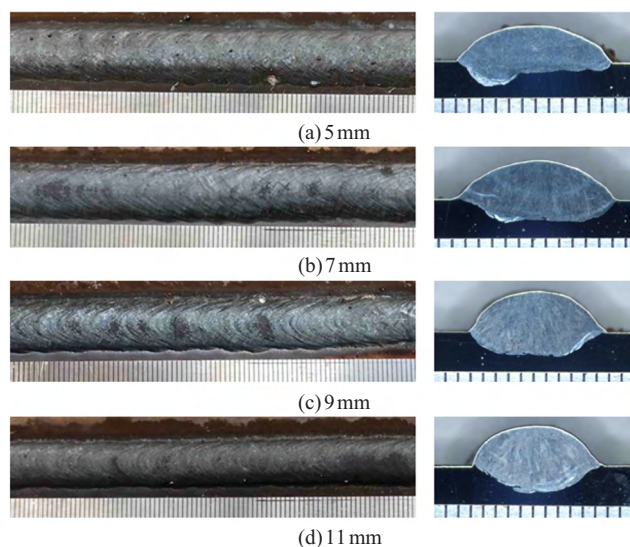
不同钨极与焊丝间距下的焊缝成形和焊缝截面
